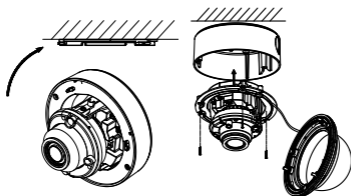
Установка камеры на потолок (Слева) Камера II типа (Справа) Камера III типа
